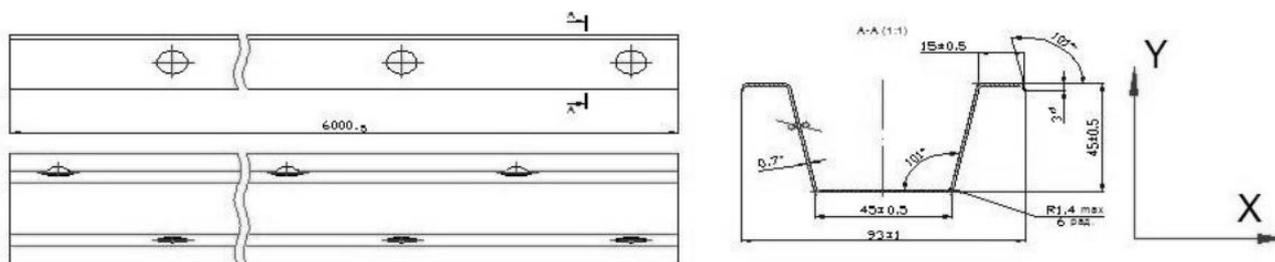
ОУВ – обрешетка универсальная вентилируемая
